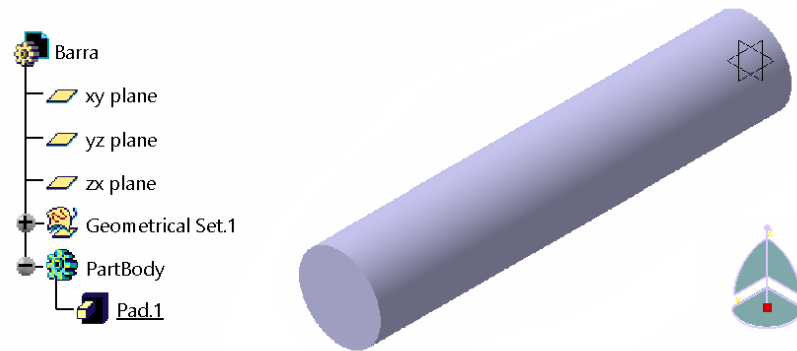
Barra creada en el módulo de Diseño Mecánico.
